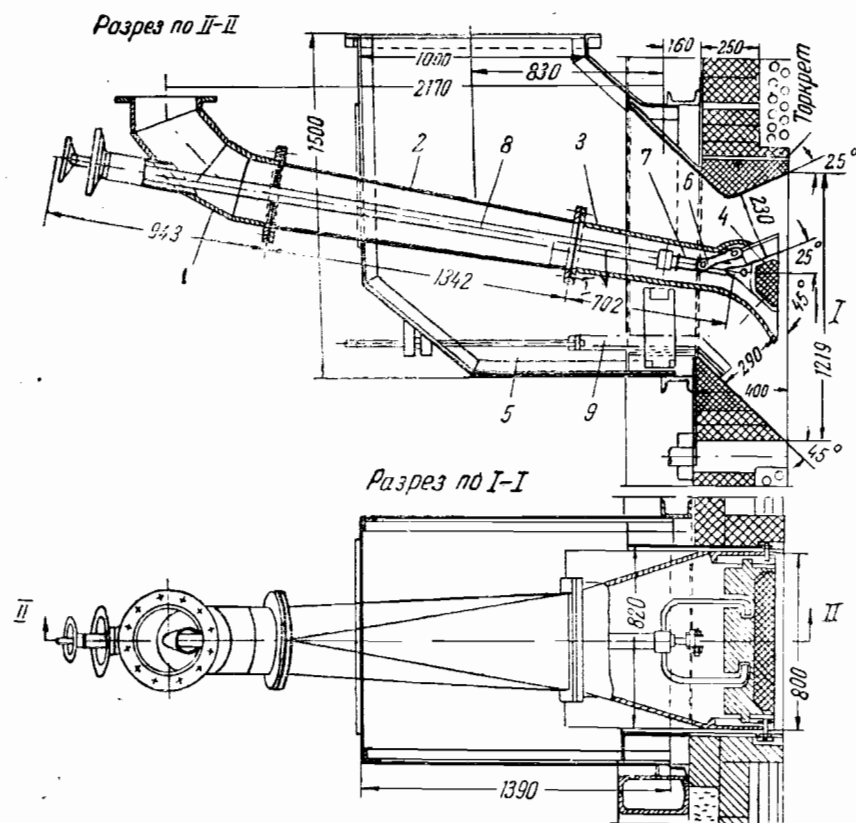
Щелевая горелка Оргрэс—БПК с рассекателем: 1—подводящее колено; 2—переходной патрубков; 3—чугунный раструб; 4—рассекатели; 5—короб вторичного воздуха; 6—рычажная передача; 7—шток; 8—труба; 9—шибер
